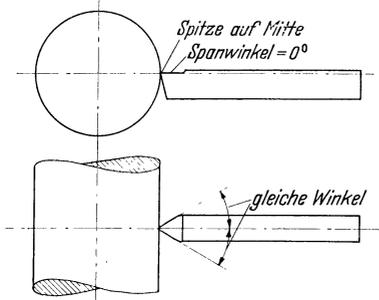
Lage des Werkzeugprofils zur Maschinenachse.
